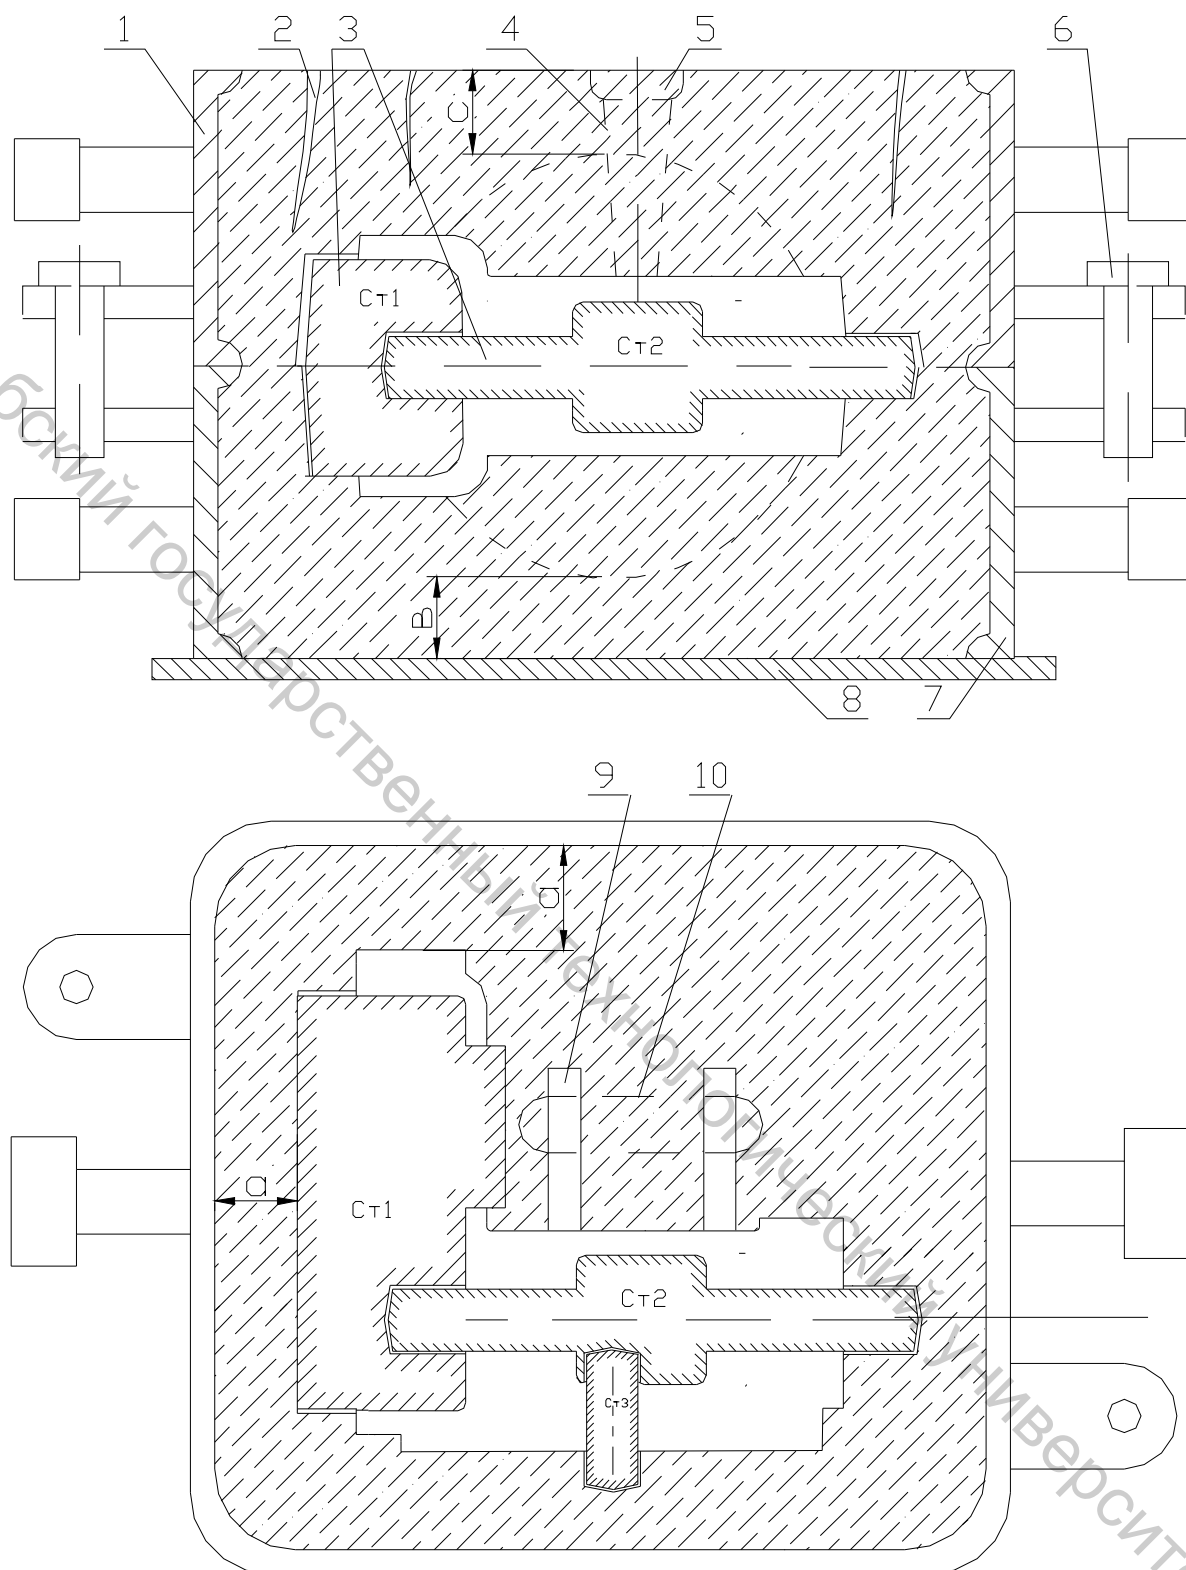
Схема ориентации отливки рассматриваемой детали в опоках:
